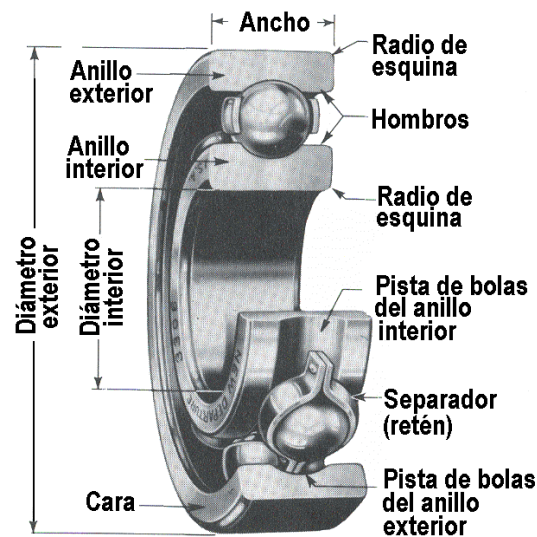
8 Componentes de un cojinete de contacto (Diseño en ingeniería mecánica de Shigley. Budynas)
